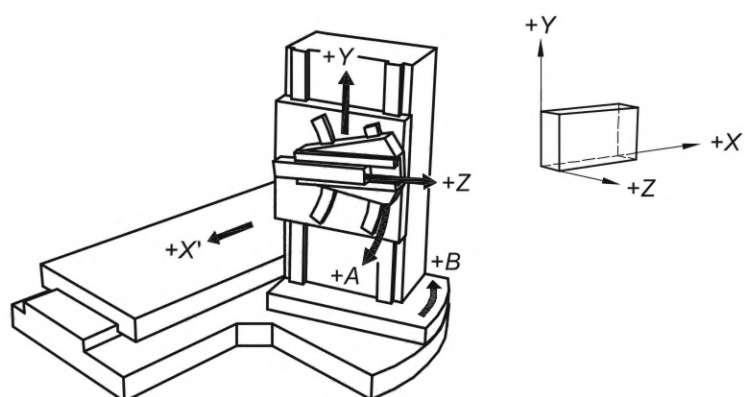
Контурно-фрезерный станок с подвижным столом
